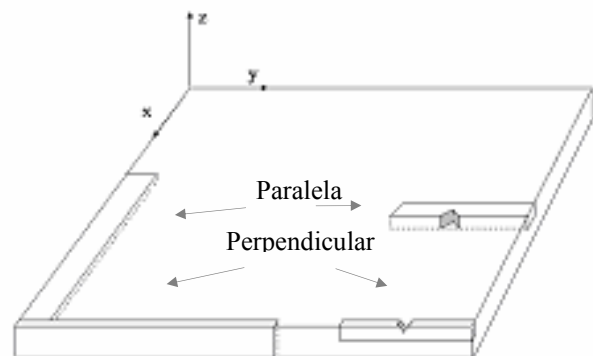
Probetas para ensayos de flexión y fractura mecanizadas en dirección paralela o perpendicular a la superficie del molde.
